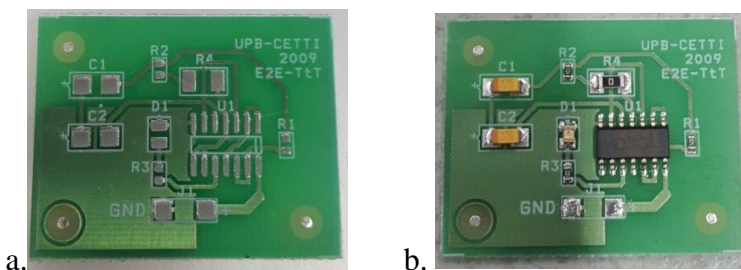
1. Exemplu de a. PCB printat și b. Ansamblul plăcii de cablaj imprimat
